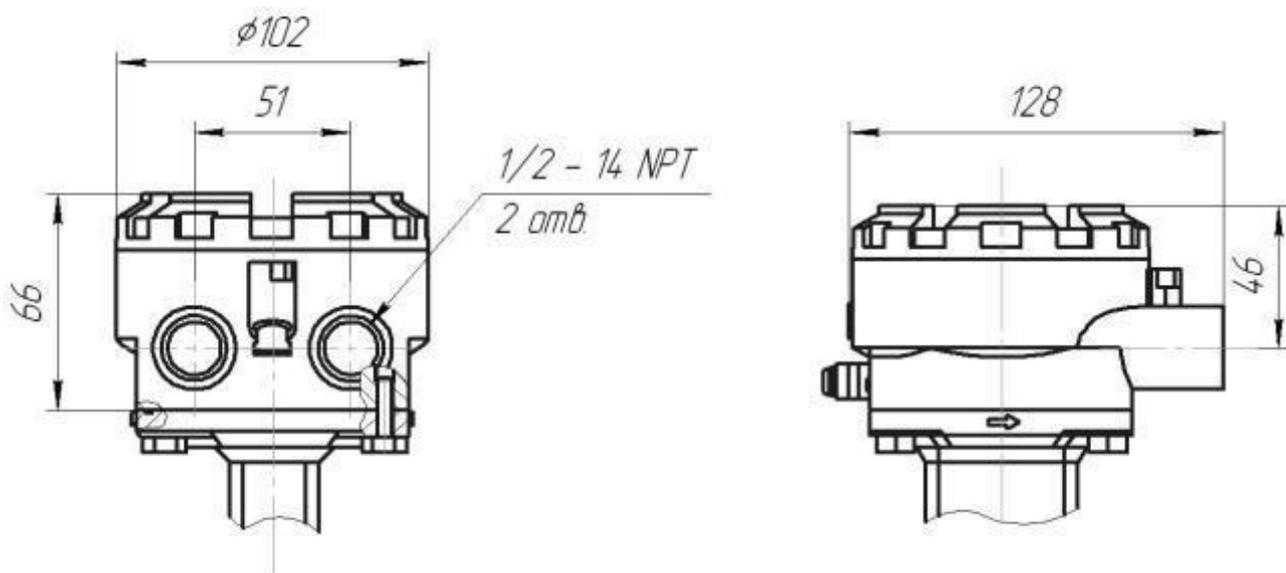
Габаритные размеры соединительной коробки для удаленного монтажа датчика расхода
